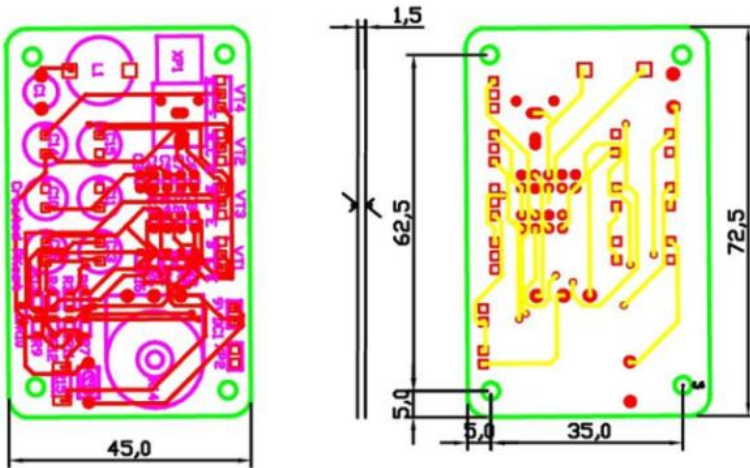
Трасована плата в програмі P-CAD PCB.
